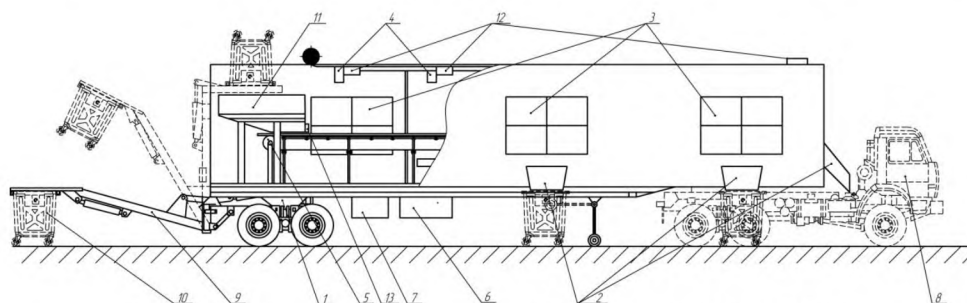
Общий вид комплекса сортировки ТБО.
